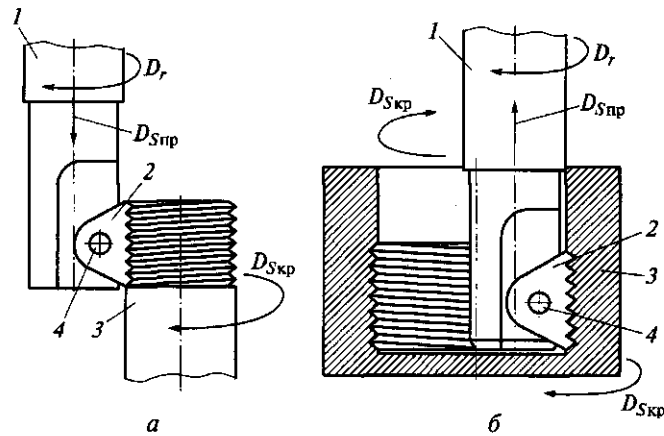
Резьбофрезерование на станках с ЧПУ наружной (а) и внутренней (б) резьбы:
